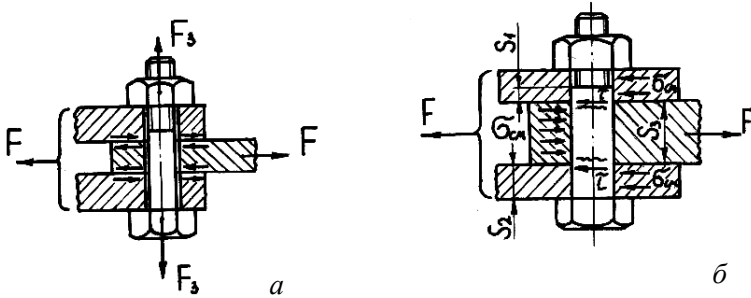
К расчету болта, нагруженного поперечной силой:
